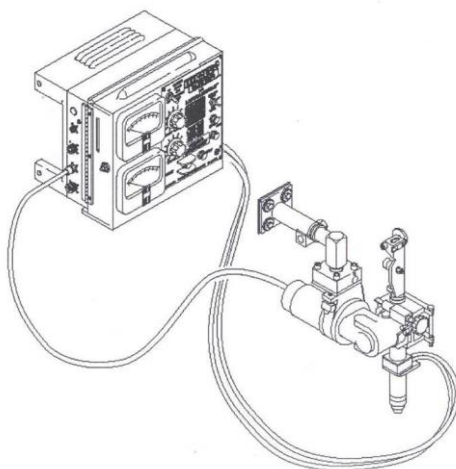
Головка для автоматической сварки и блок управления
